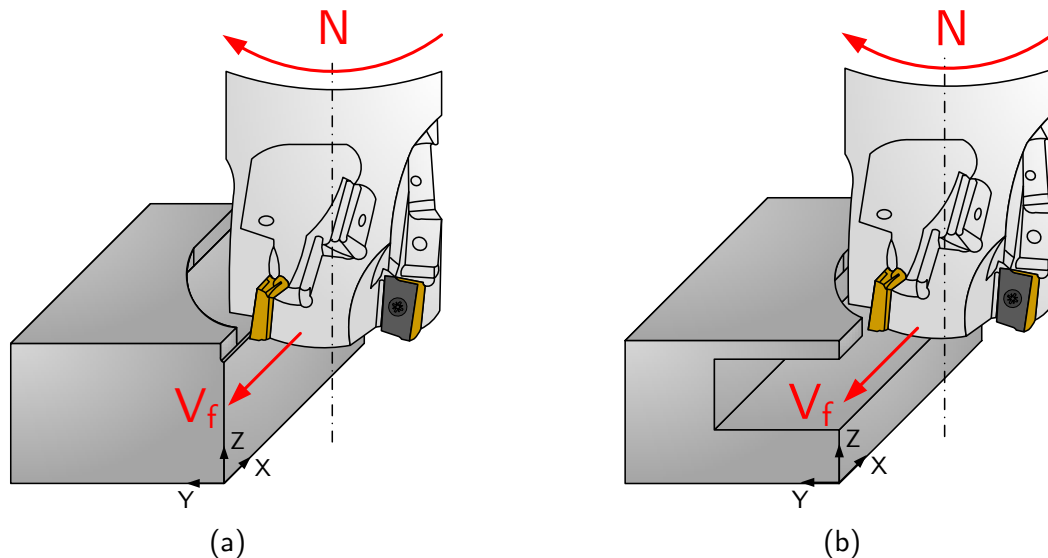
Configurations d'essais en (a) fraisage épaulé (usinage en bout) ; (b) fraisage de profil pur (usinage sur flancs) avec bord extérieur de l'éprouvette dans la direction d'avance préalablement rayonné
